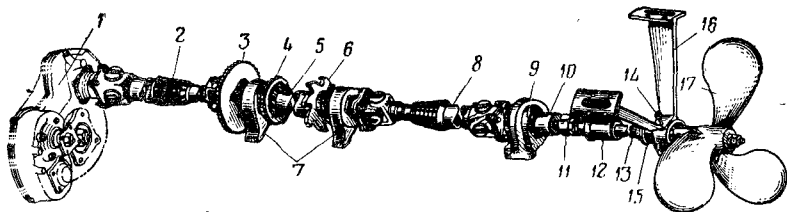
Гребной винт и привод винта плавающего автомобиля БАВ: 1 — коробка отбора мощности; 2, 5 и 8 — карданные валы; 3 — звездочка привода водооткачивающего трюмного насоса; 4 — звездочка привода водооткачивающего насоса отсеков; 6 — храповик; 7 — промежуточные опоры; 9 — опора; 10 — упорная муфта гребного вала; 11 — гайка корпуса уплотнителя; 12 — шланг уплотнителя выхода гребного вала; 13 — вал гребного винта; 14 — масленка; 15 — отражатель опорного подшипника; 16 — кронштейн гребного вала; 17 — гребной винт
